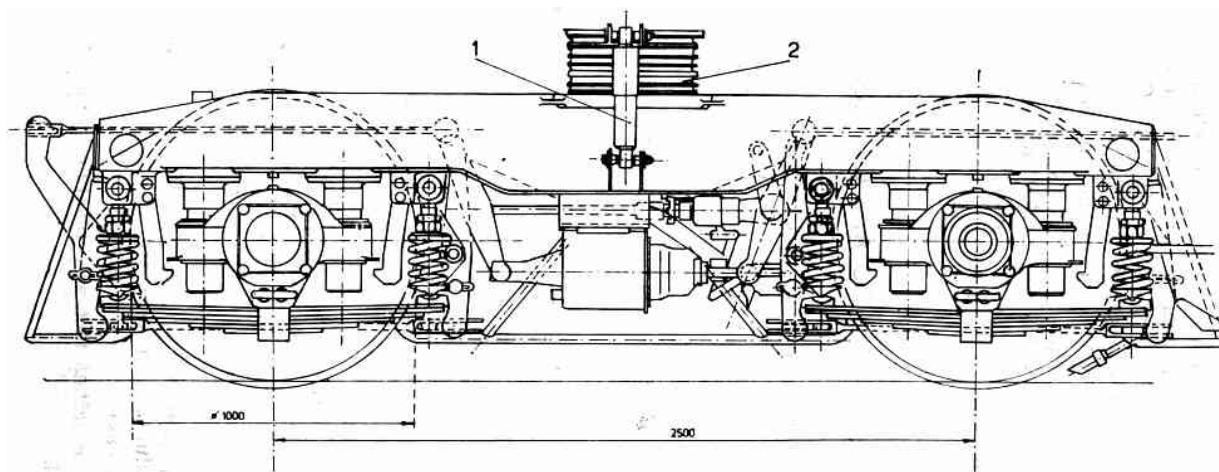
Boghiu de locomotivă diesel hidraulică de 1250 CP
